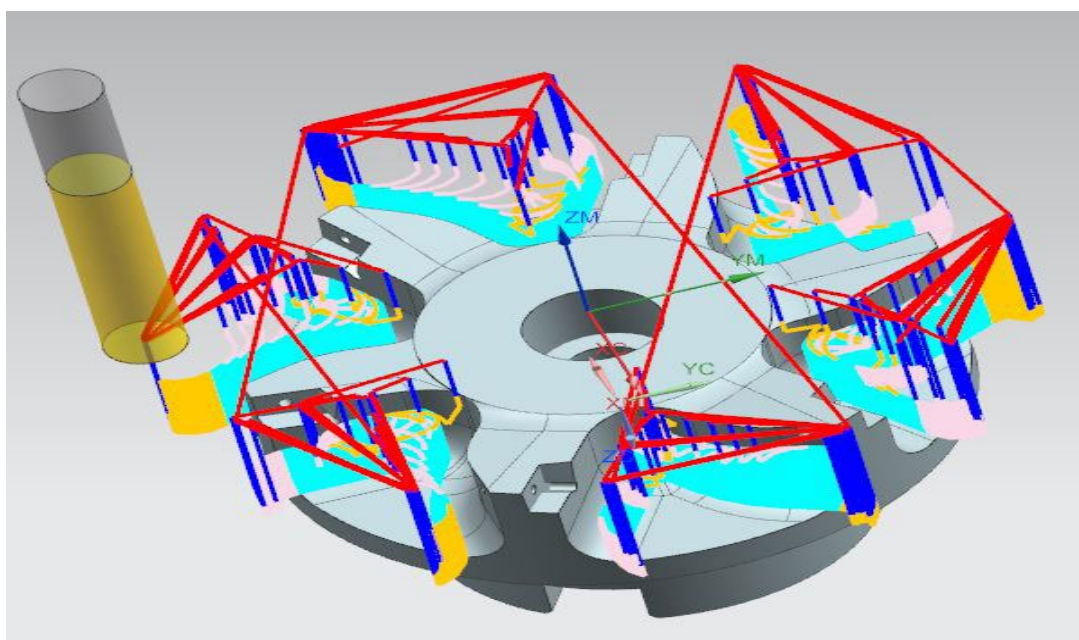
Схема обработка фрезы на станке с ЧПУ
